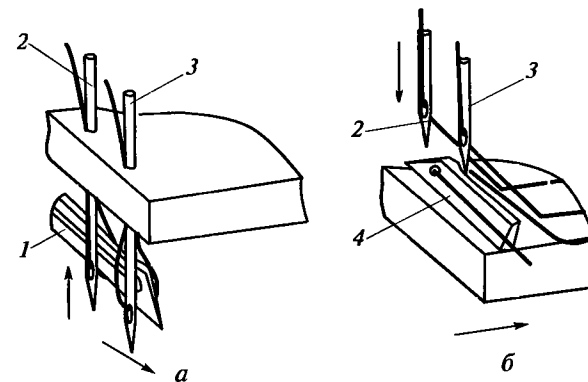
Схемы образования четырехниточного краеобметочного стежка типа 512:
